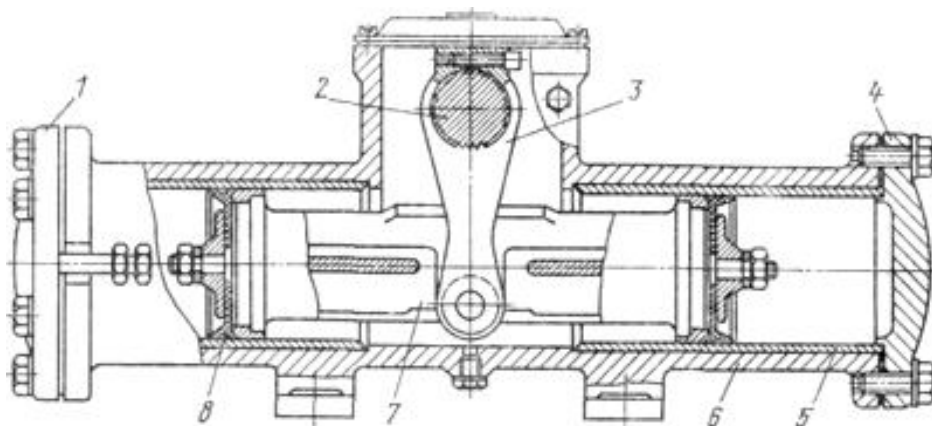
Поршнерычажный поворотный пневмодвигатель
